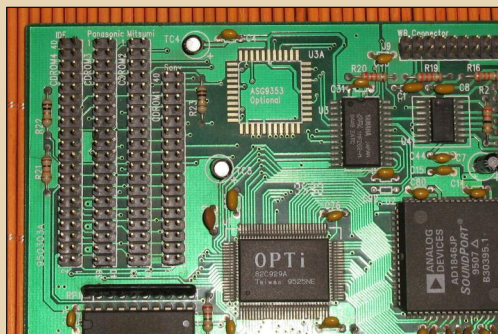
Фрагмент звуковой платы AD1846 с разными встроенными контроллерами приводов компакт-дисков
